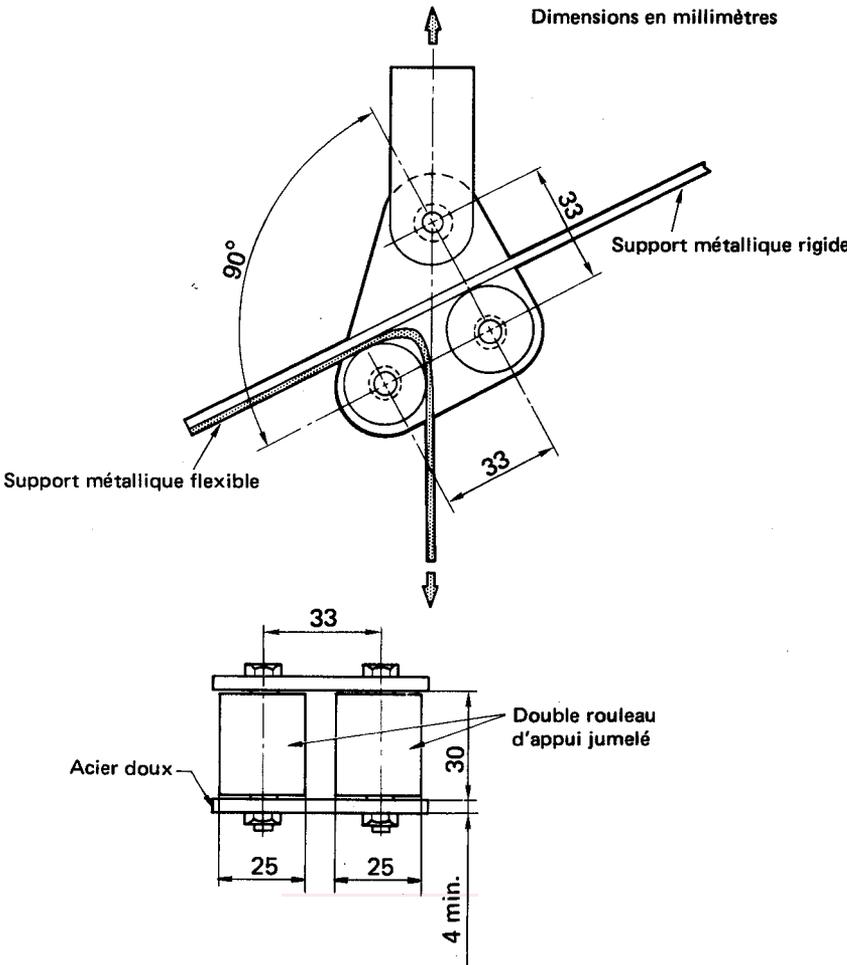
Dispositif destiné à supporter l'éprouvette
